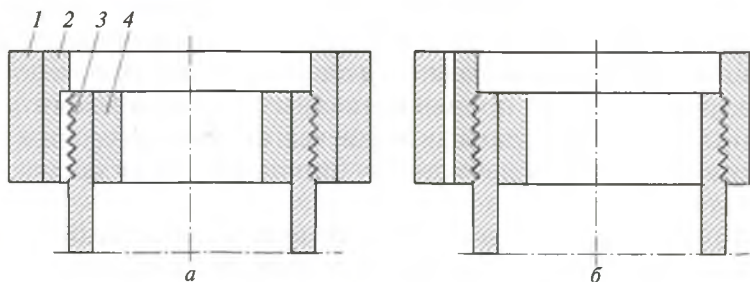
Схема получения клинопрессовой сваркой соединения законцовки из алюминиевого сплава Д20 с КМ боралюминий с продольным и окружным армированием:
